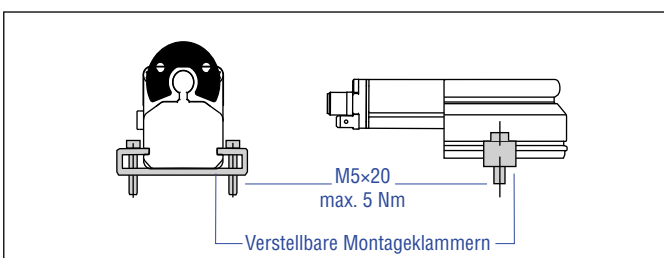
EP mit Montageklammern mit Zylinderschraube M5×20 (Artikelnr. 403 508)
